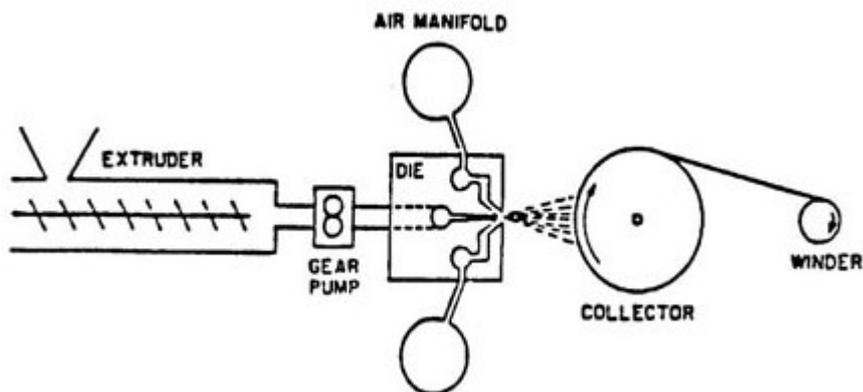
Processo Meltblowing. Extrusora, bomba de engrenagens (gear pump), matriz (die), distribuidores de ar (air manifold), esteira coletora (collector) e rolete bobinador (winder).
